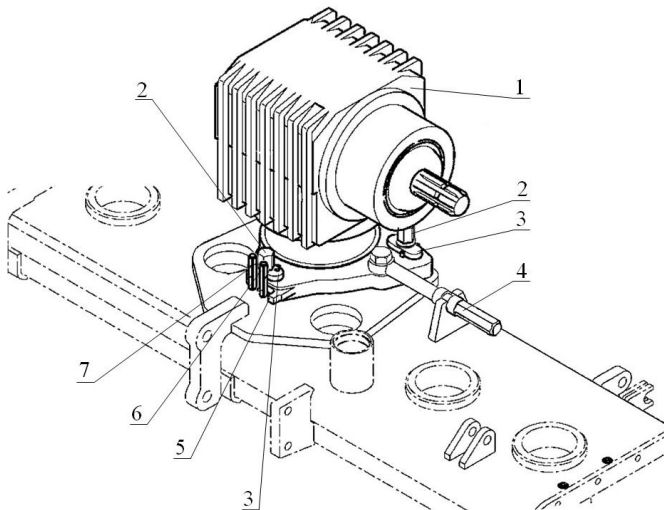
Регулировка направления вращения: 1 – редуктор; 2 – гайка; 3 – эксцентрик; 4 – винт; 5 – указатель положения; 6, 7 – штифты.
